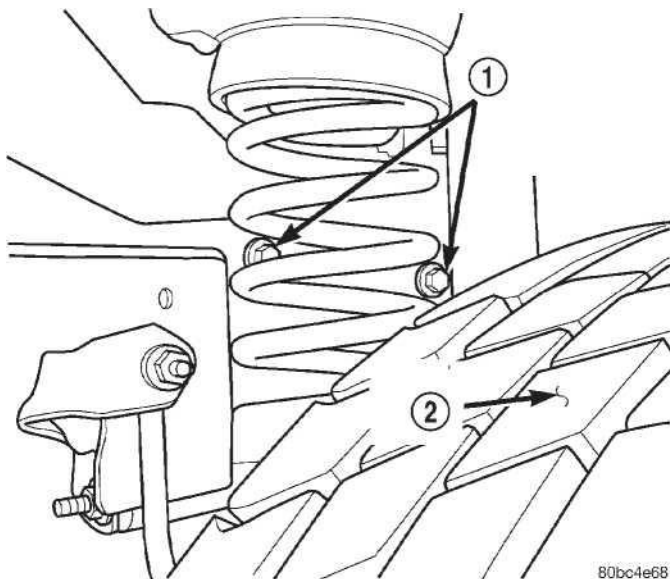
Болты пластины подоконника опоры двигателя - левое колесо хорошо
